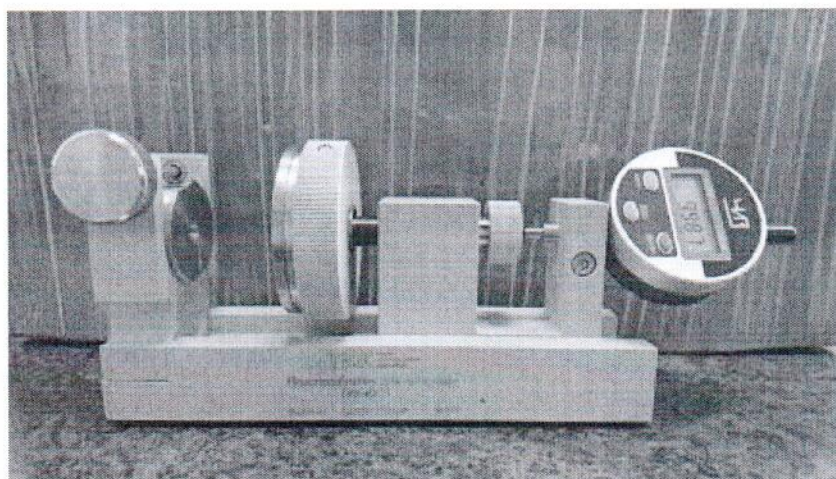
Общий вид устройства для поверки и настройки вихревых преобразователей ТИК-ЮСТ с цифровым индикатором
